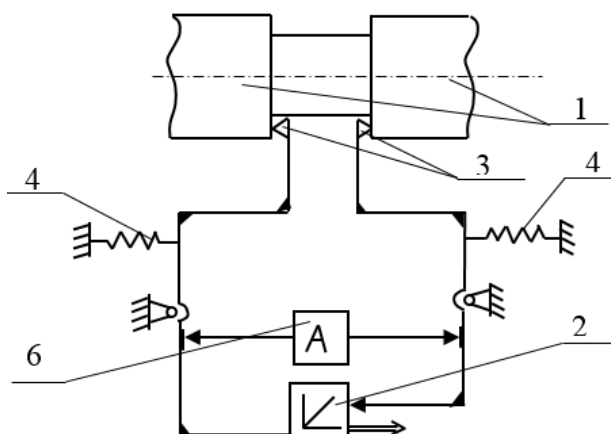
Вимірювальний пристрій для контролю відстані між торцями деталі
